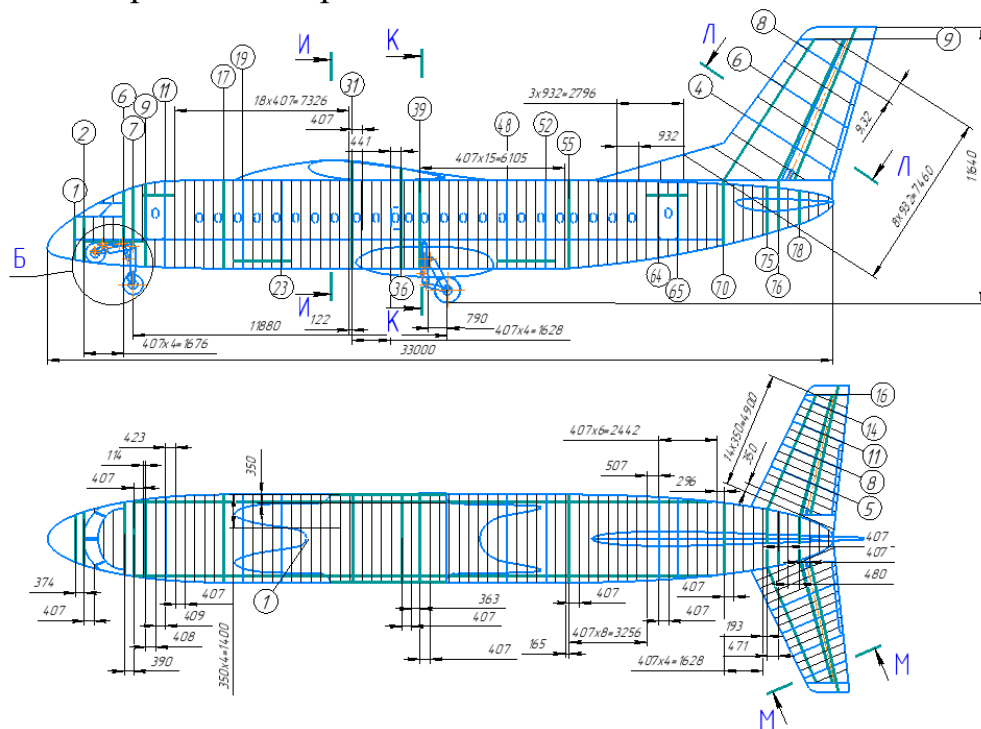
Конструктивно-силова схема фюзеляжу
